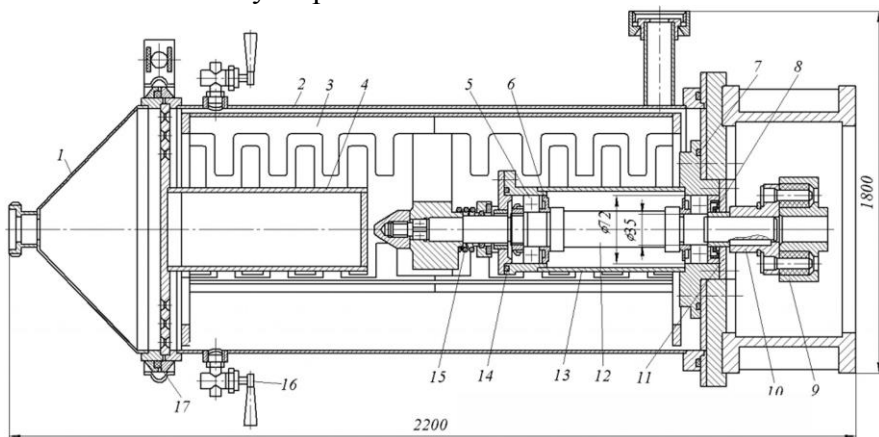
Загальний вид маслообробника маслоутворювача марки РЗ-ОУА1: 1 - конус маслообробника; 2 - циліндр; 3 - мішалка; 4 - відбивач; 5 - підшипник; 6, 7 - кільце; 8 - манжета; 9, 10 - напівмуфта; 11 - кришка; 12 - вал; 13 - кільце; 14 - ущільнення; 15 - пружина; 16 - кран пробно-спускний; 17 - кільце
